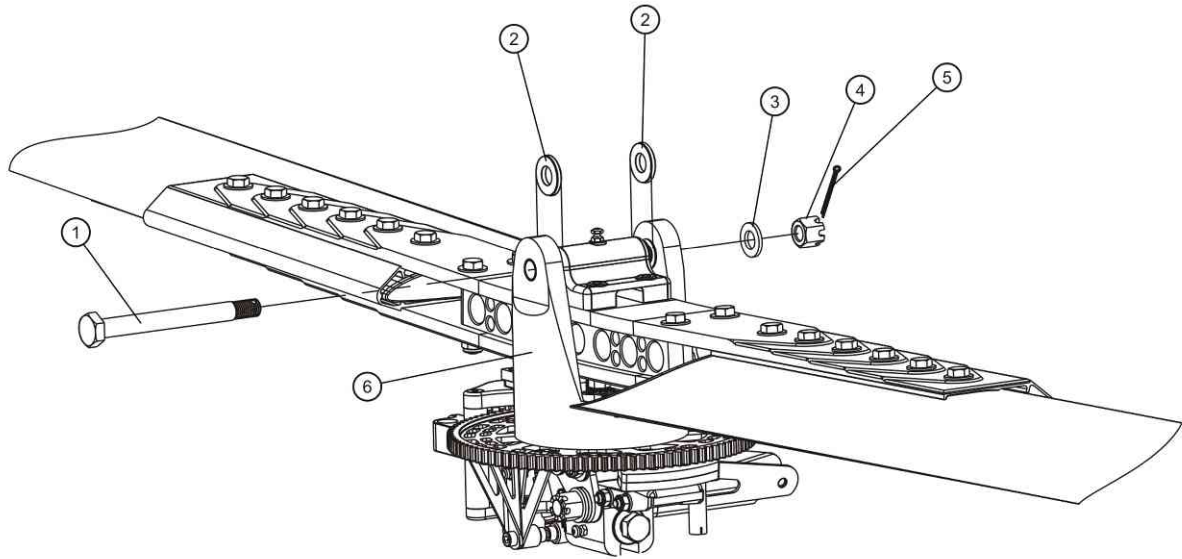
Einbau Rotor - schwenkgelagerte Teile
